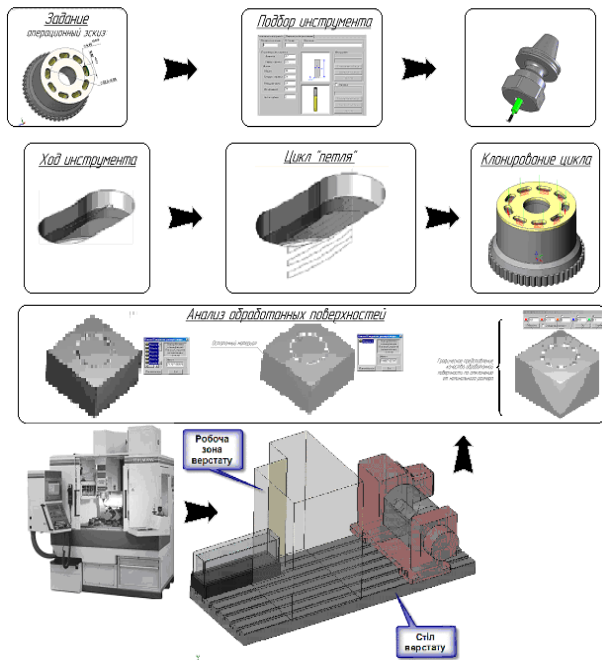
Система підготовки керування верстатами з ЧПК (САП) SolidCAM
